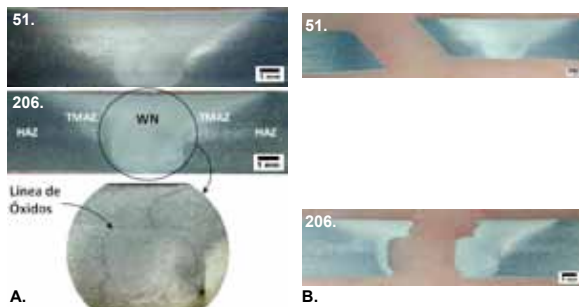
Macrografías de uniones 51 y 206: a) Como soldadas. b) Traccionadas.
